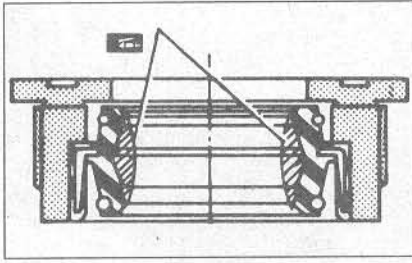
Установочные детали поджимной гайки набивного сальника стойки (Глава 15)
